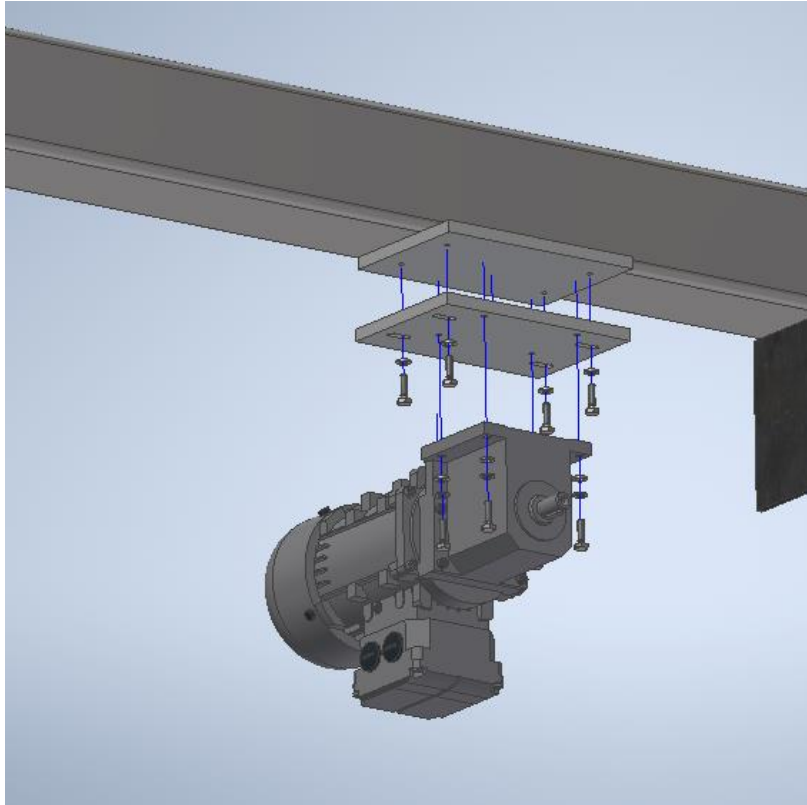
Vista explosionada montaje del motorreductor con placa de ajuste.
